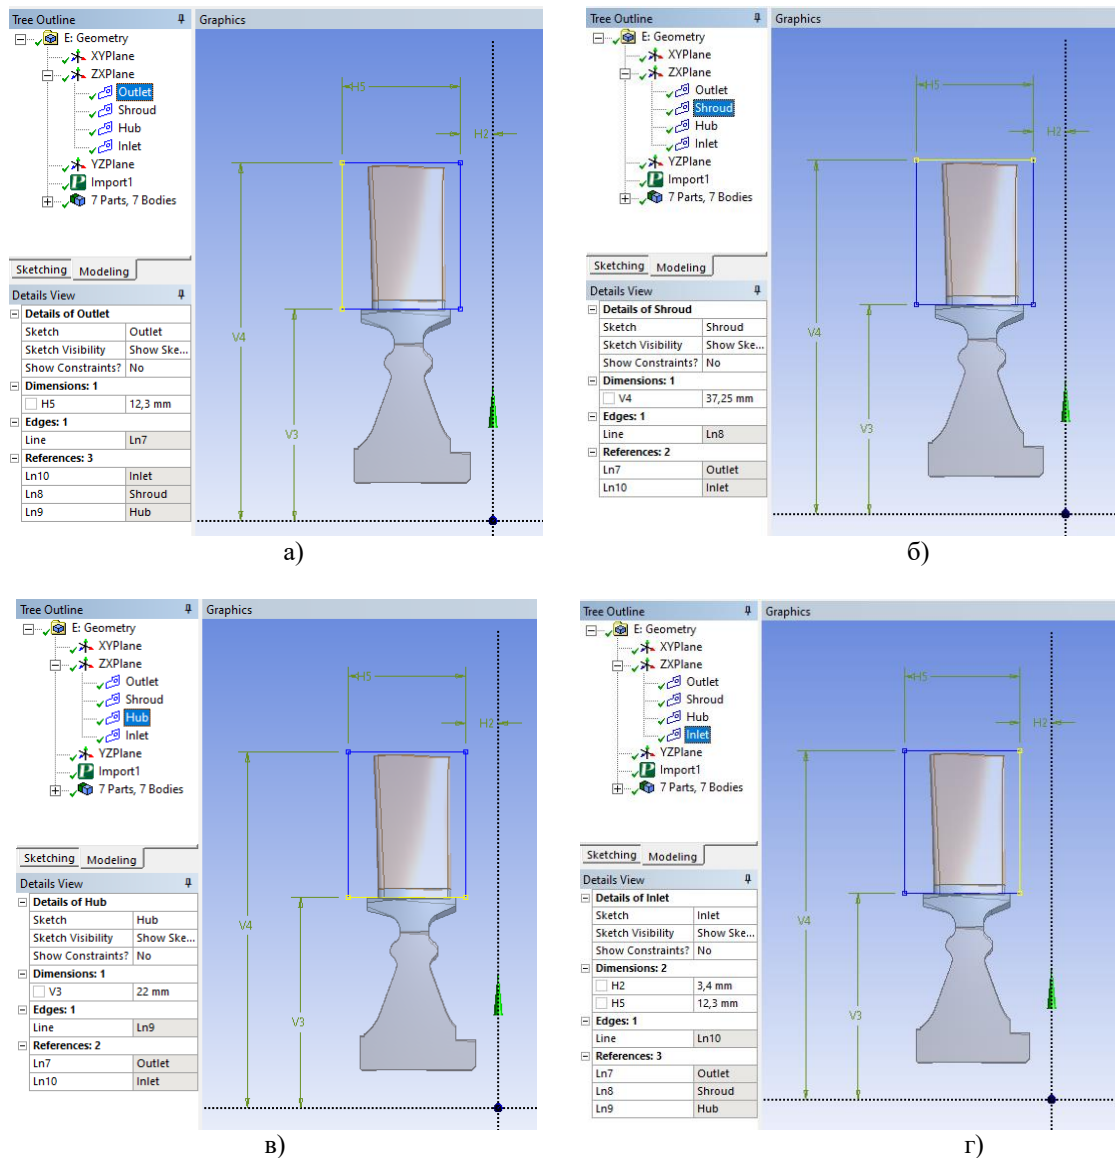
Эскизы и размеры проточной части рабочего колеса:
